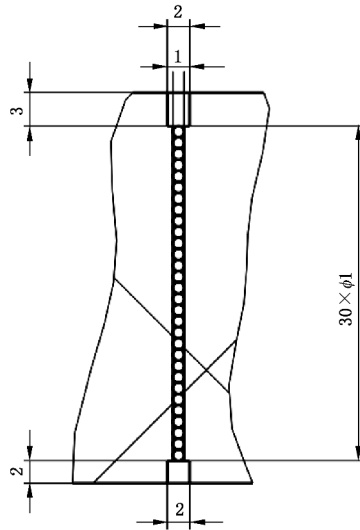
30 颗直径为 1 mm 的钢珠装配图
